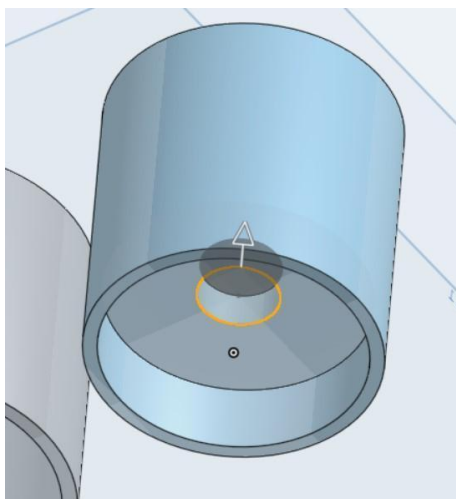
Вид осі з отвором для підшипника і пазом для з'єднання
